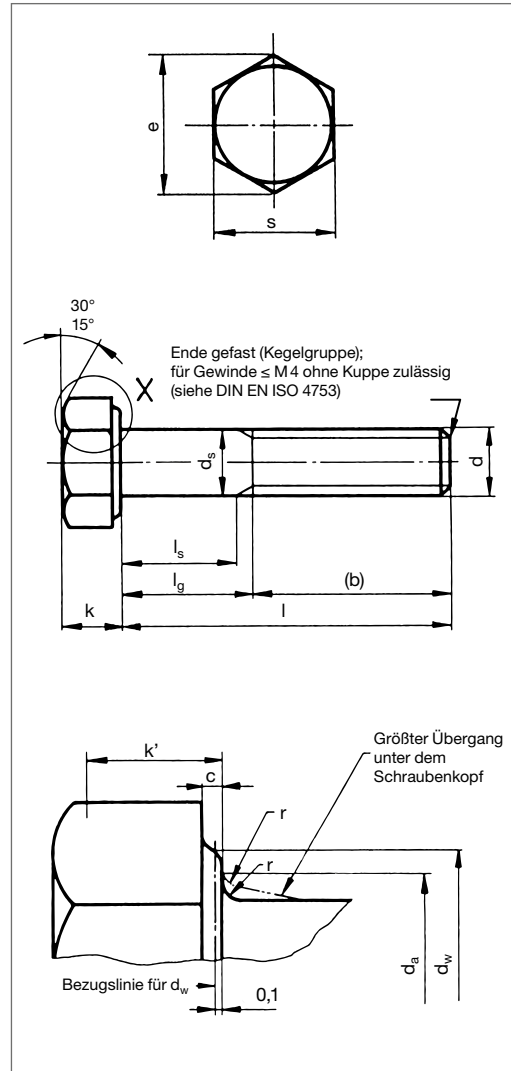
Sechskantschraube mit Schaft DIN EN ISO 4014
